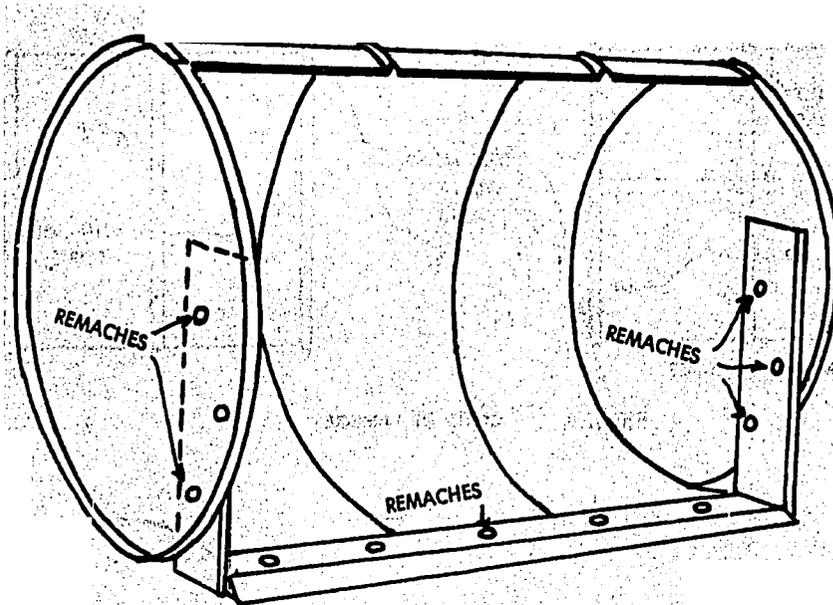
SUJECION DE LA HOJA, SIN SOLDADURA
